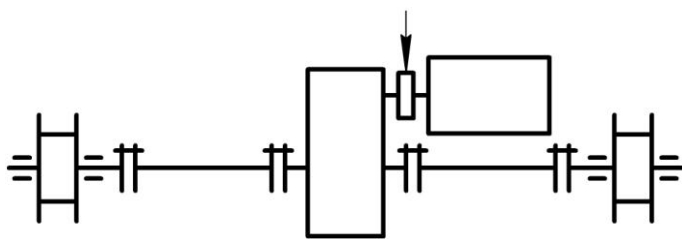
Механизм передвижения тележки с центрально расположенным редуктором
